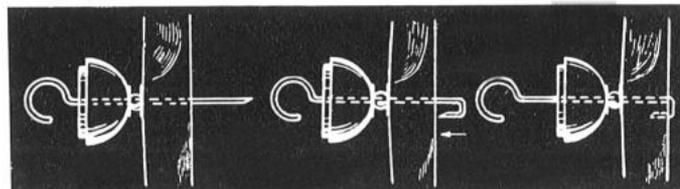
Come si procede per il fissaggio dell'asse sull'elica.
